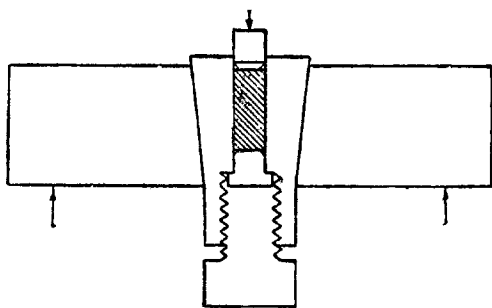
Принципиальная схема конструкции наружной оболочки («суппорта») камеры давлений, позволяющая увеличивать сопротивление оболочки по мере увеличения внутреннего давления.
